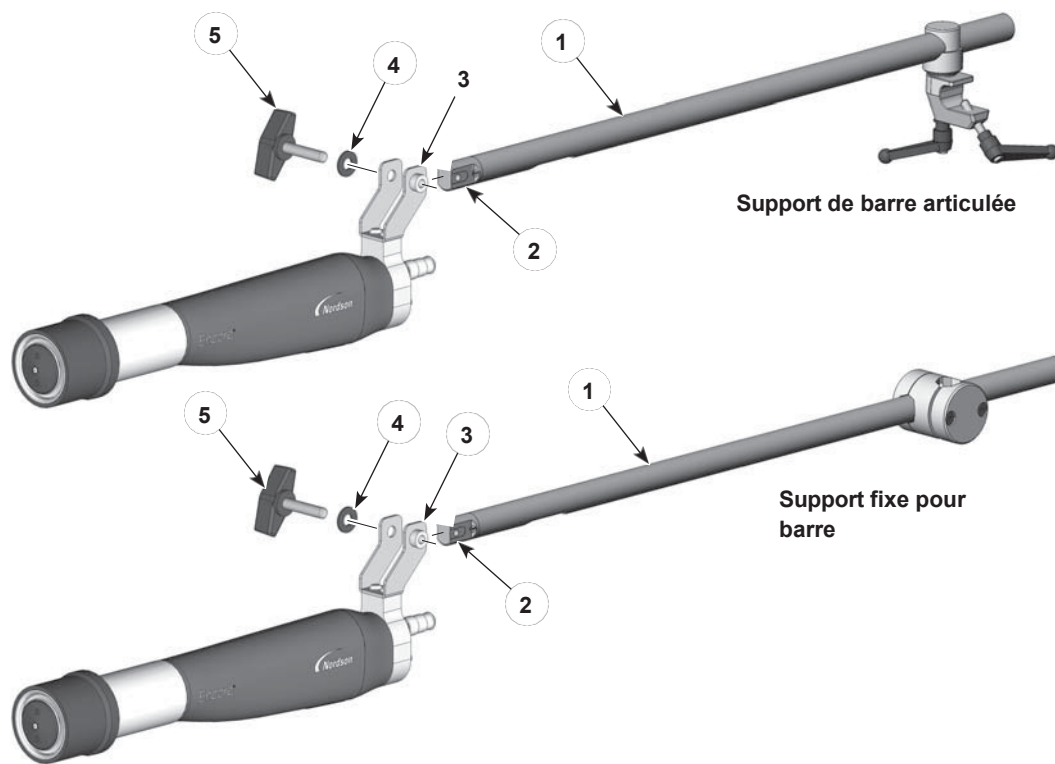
Kits de fixation pour barres de pistolet en option pour l'
